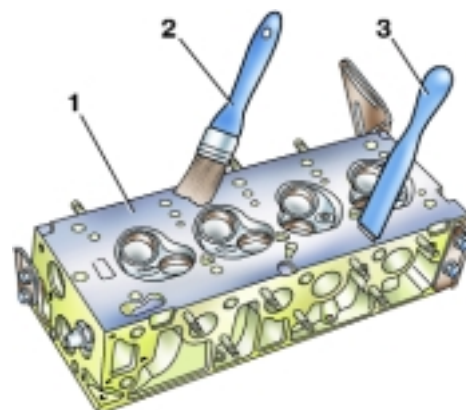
Очистка поверхности головки блока двигателя F3R 272 от остатков прокладки: 1 – головка блока; 2 – кисть; 3 – деревянная лопатка
